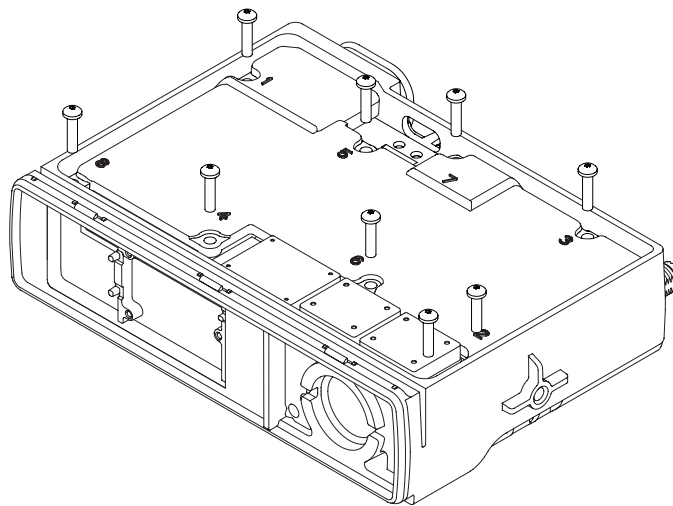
Montage de la plaque de protection moulée sur le châssis
